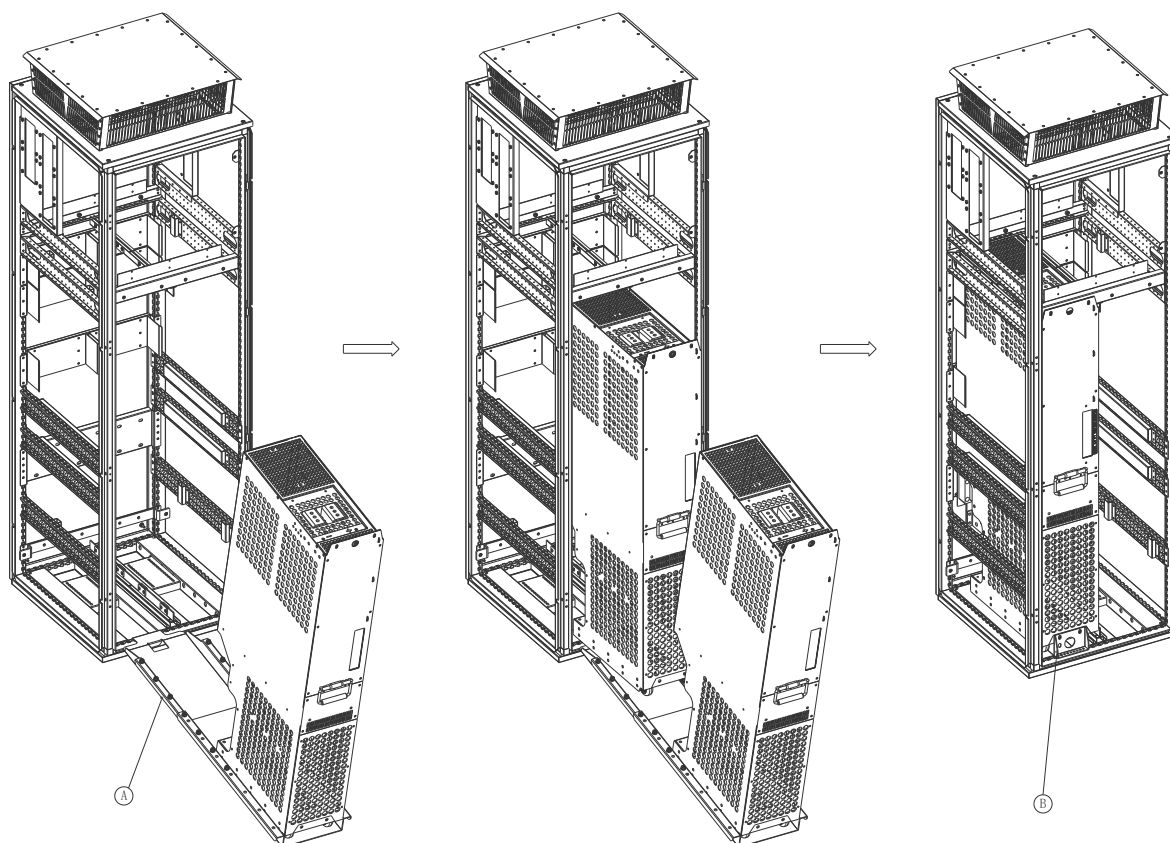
Схема последовательности действий по установке модуля корпуса FR8
